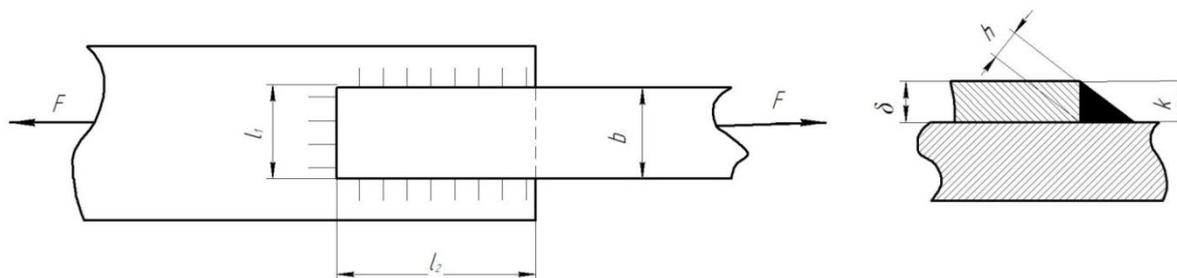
Схема сварного соединения внахлестку угловыми швами
